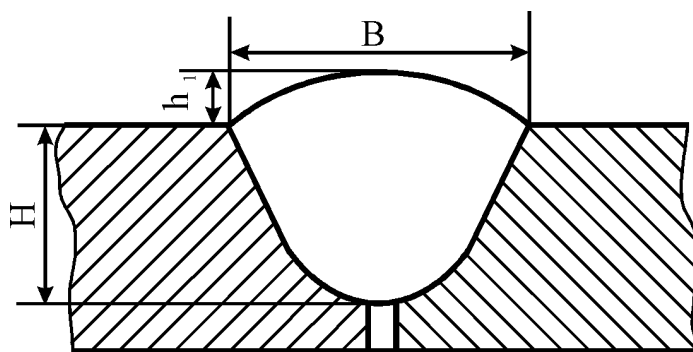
Форма поперечного сечения сварного шва стыкового соединения
